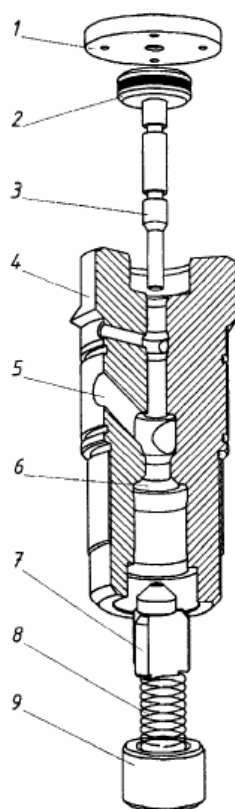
Перепускний клапан ТНВД дизеля серії МС фірми MAN : 1 - кришка; 2 - пневматичний поршень; 3 - шток; 4 - корпус клапана; 5 - перепускний канал; 6 - сідло клапана; 7 - клапан; 8 - пружина; 9 - пробка.
